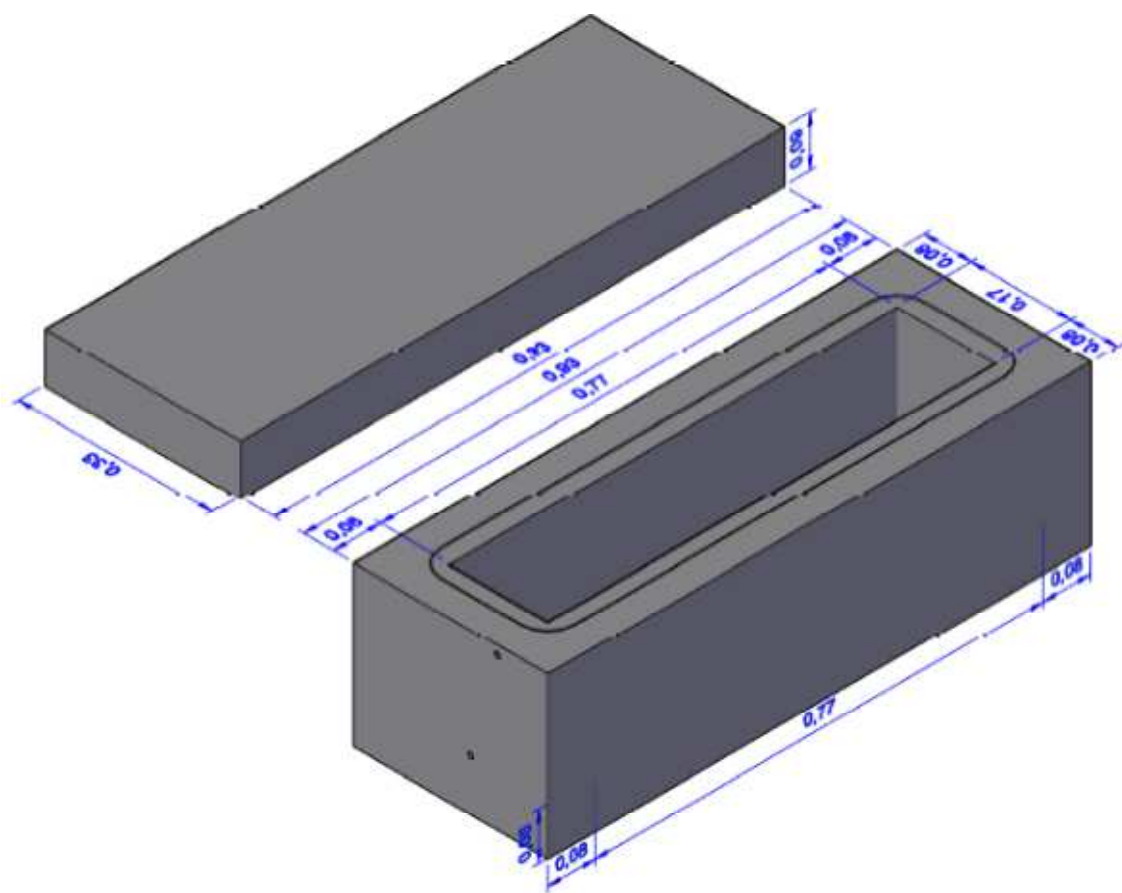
Planta de caixa térmica com isolamento térmico
